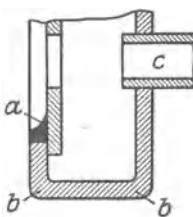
Unterer Teil einer neueren Ausführung der Wasserkammer. Die älteren Wasserkammern haben bei b Schweißstellen, die schwierig auszuführen waren und durch Aufreißen zu Kesselexplosionen Anlaß gaben. Die Schweißstelle a der neueren Wasserkammern ist sicherer herzustellen, c = die unterste Reihe der Siederöhre.
